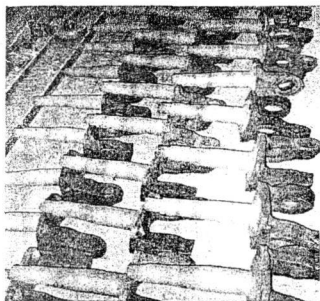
Поворотные кулаки троллейбуса. Посадочные места под подшипники напылены проволокой 20X13
